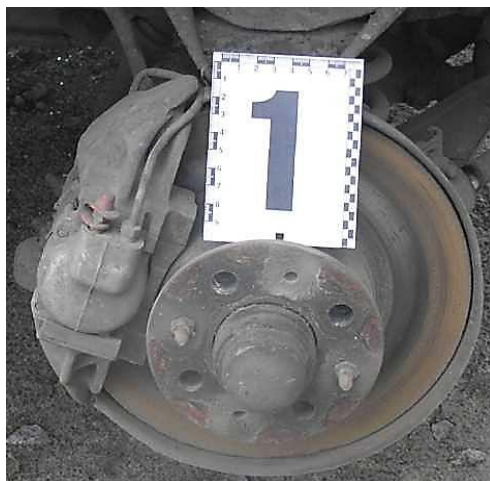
Загальний та детальний вигляди збоку гальмівного механізму правого переднього колеса
